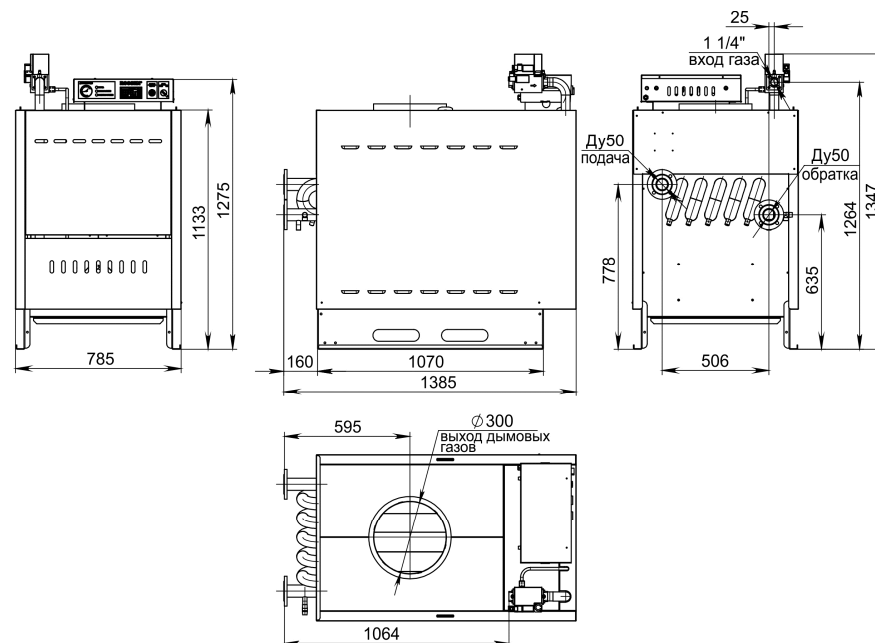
Габаритно-присоединительные размеры котла RSA200
